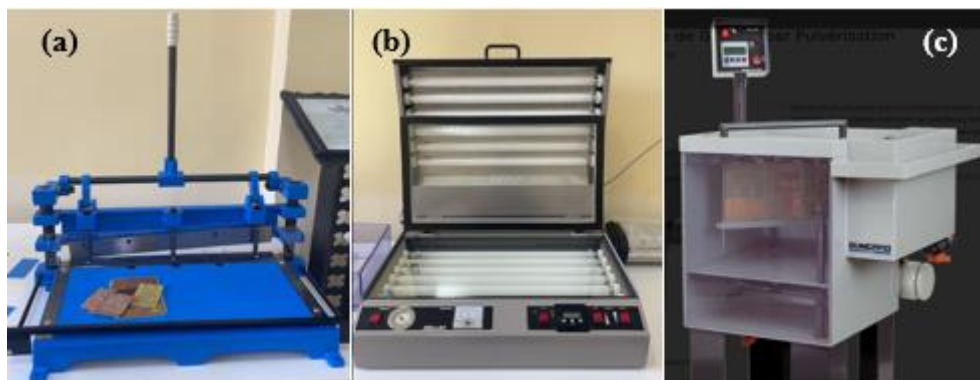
matériels utilisés pour la fabrication. (a) : appareil de coupage. (b) : machine à ultraviolet. (c) : machine à gravure.
